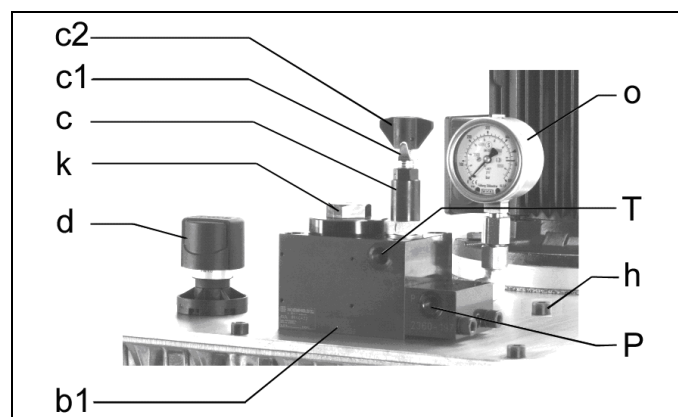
Groupe hydraulique avec bloque de connexion et filtre haute pression
